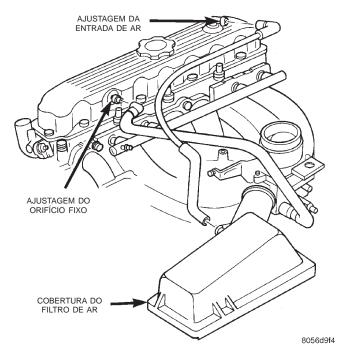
Tampa do Cabeçote de Cilindros do Motor
